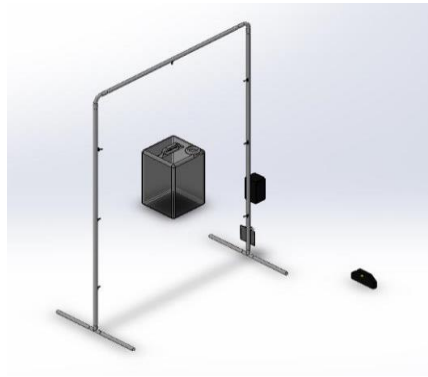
Diseño CAD de arco Sanitizante ensamblado
